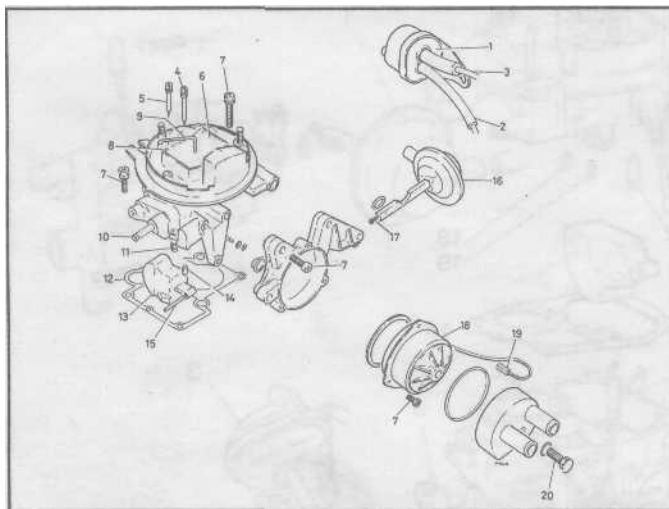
, б. Детали верхней крышки карбюратора Pierburg / Solex 183;1
